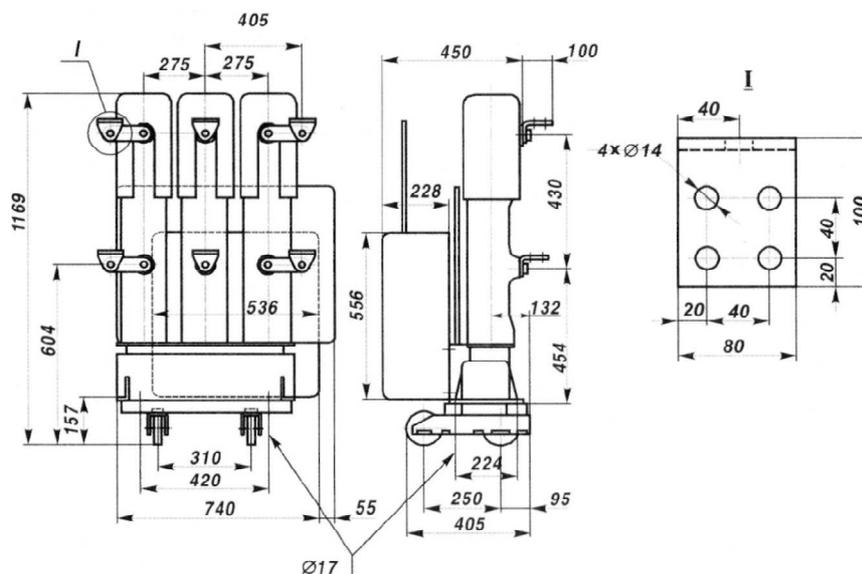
Геометрические размеры выключателя типа ВФ-12-38 кВ
